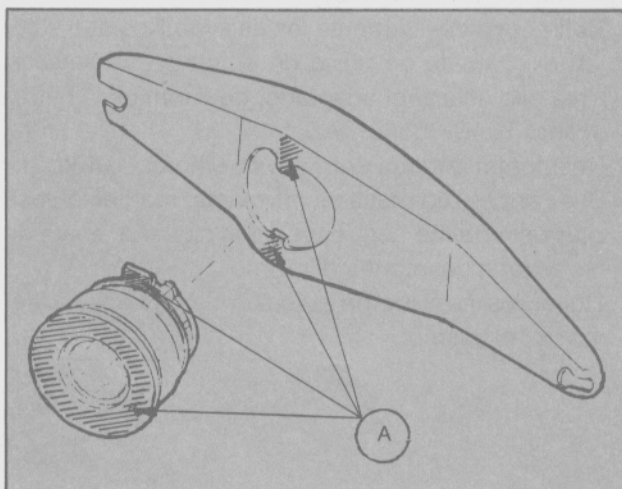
Instalación del cojinete de empuje en la horquilla de desembrague.
